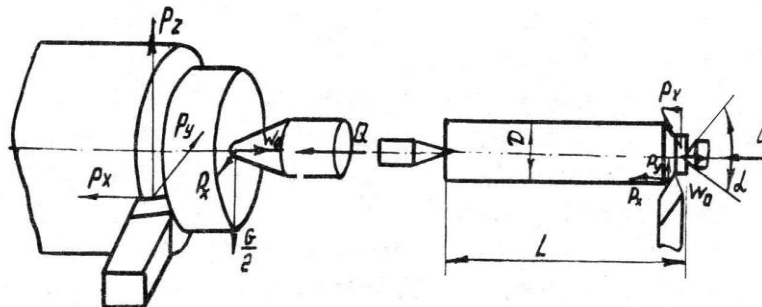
Схема установки, базування та закріплення заготовки в центрах
